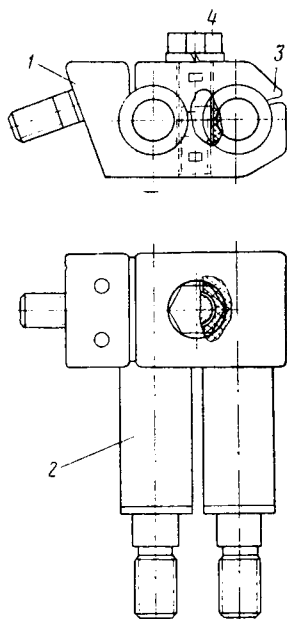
Кронштейн щеткодержателя двигателя НБ-418К6
